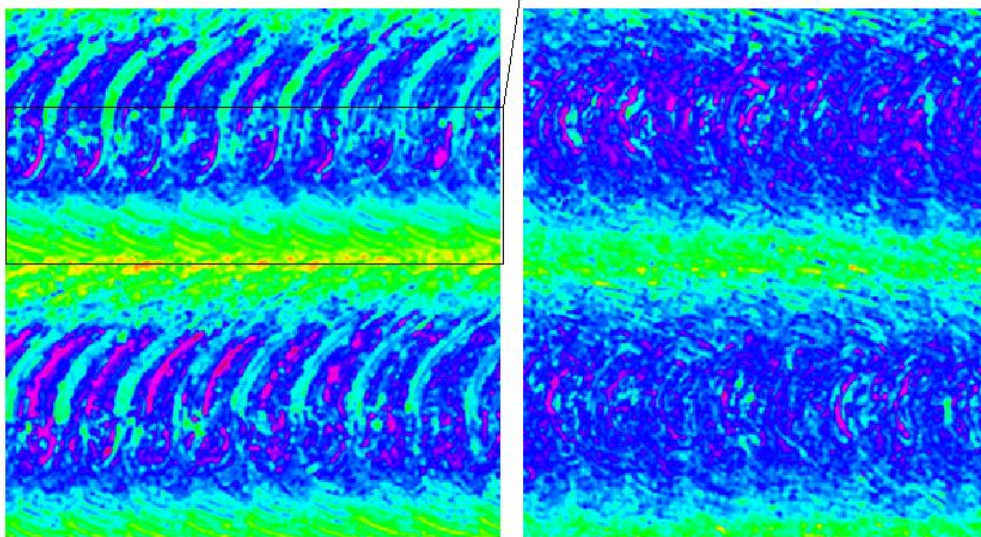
Povrch po obrobení nástrojem 5
